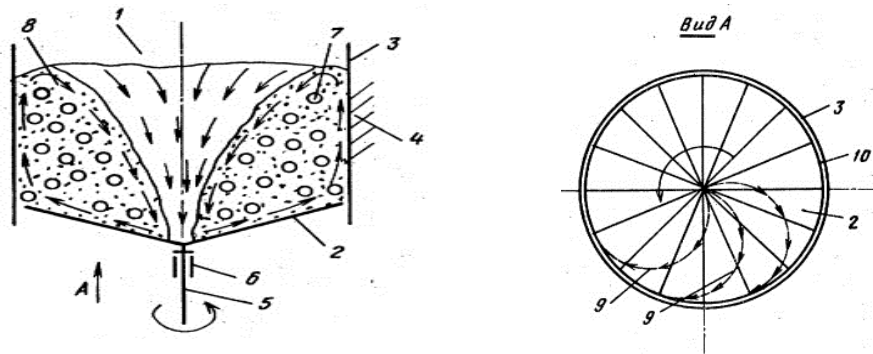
Відцентрова установка для абразивної поверхневої обробки деталей малої маси:
